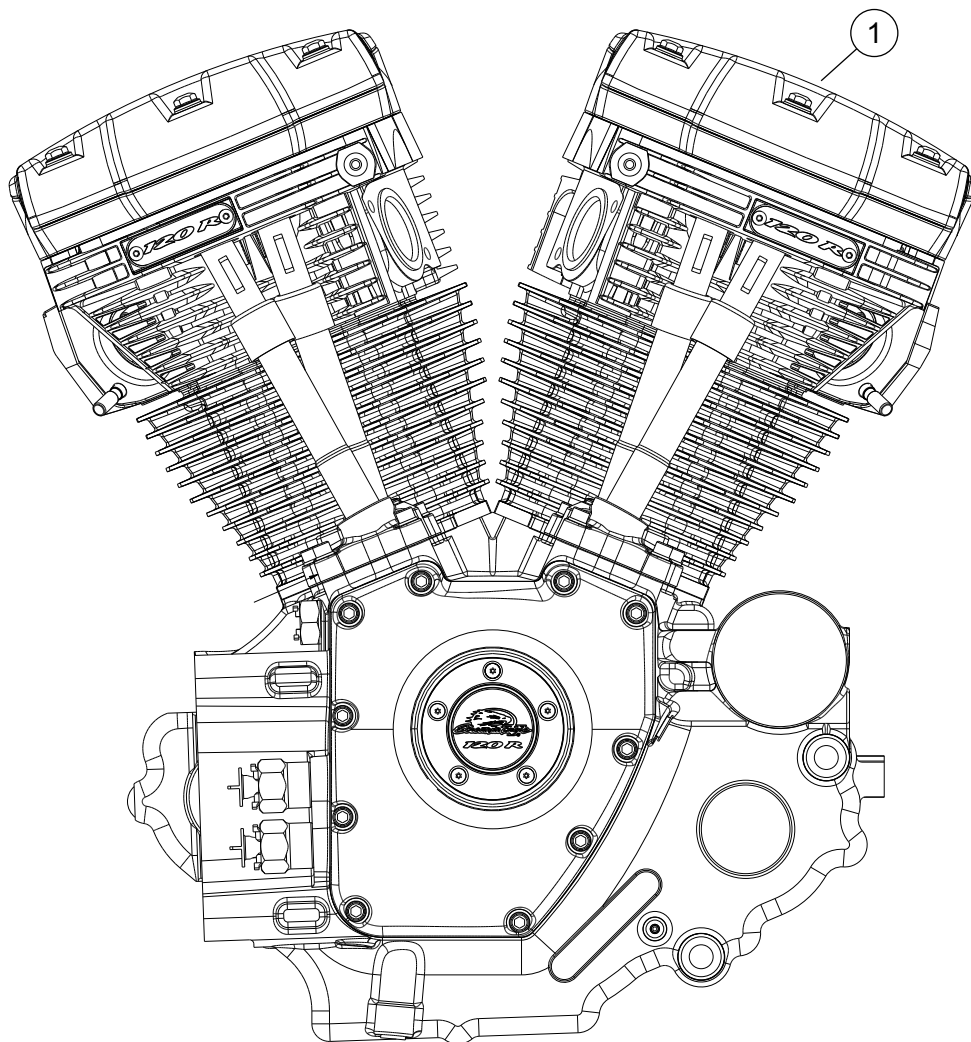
Gruppo motore, motore preassemblato Screamin' Eagle Pro 120R (Beta) completo
